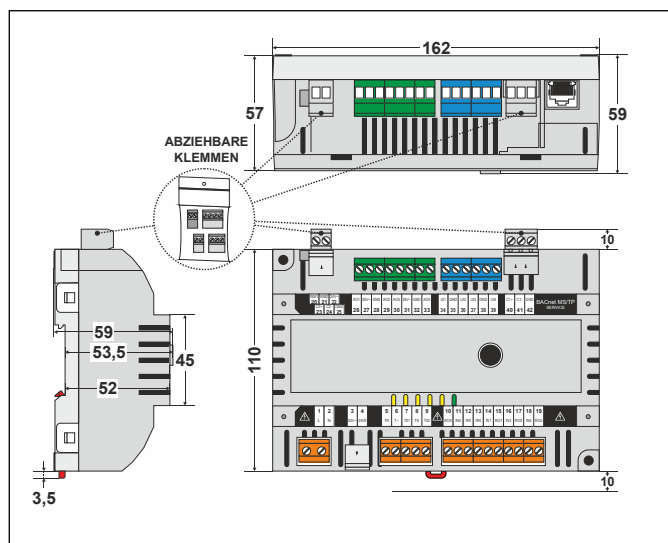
PCD7.LRSx Abmessungen (in mm)
